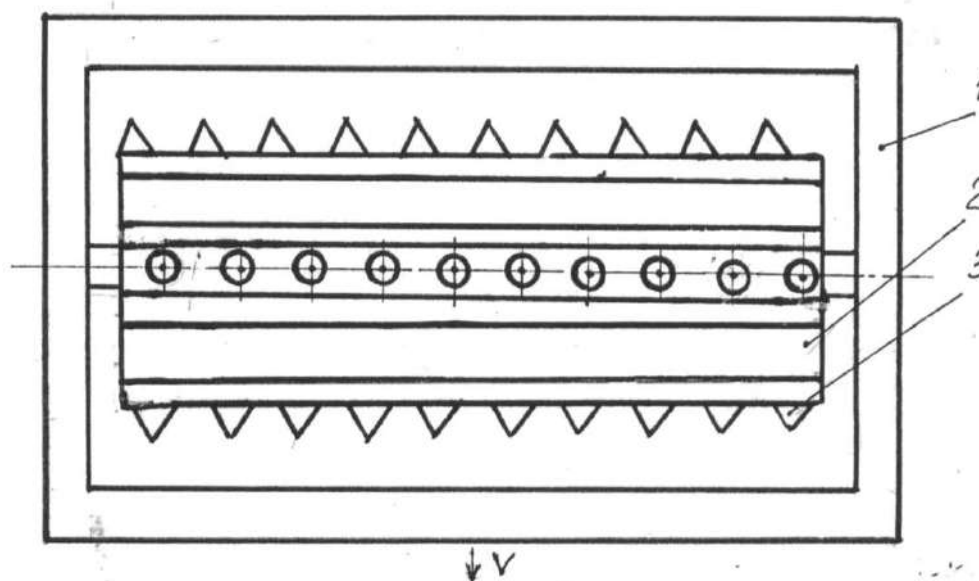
Серийный зубчато-планчато-бороночный каток.
